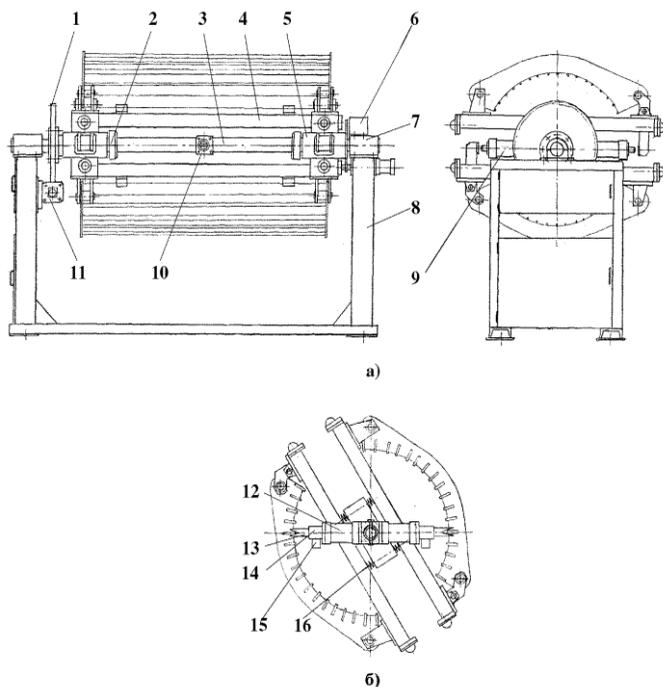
Позиционер для роботизированной сварки каркаса
